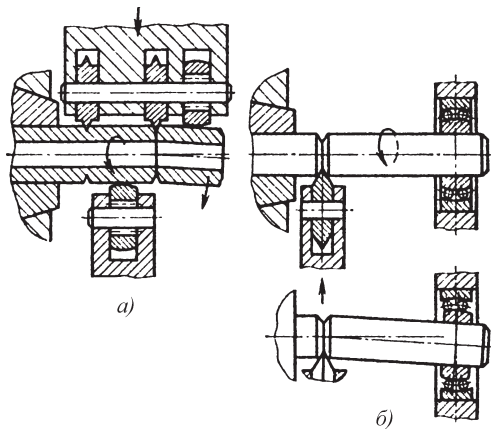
Схемы разделения круглого проката и труб на заготовки обкаткой клиновым роликом (а), обкаткой и разрушением (б)
